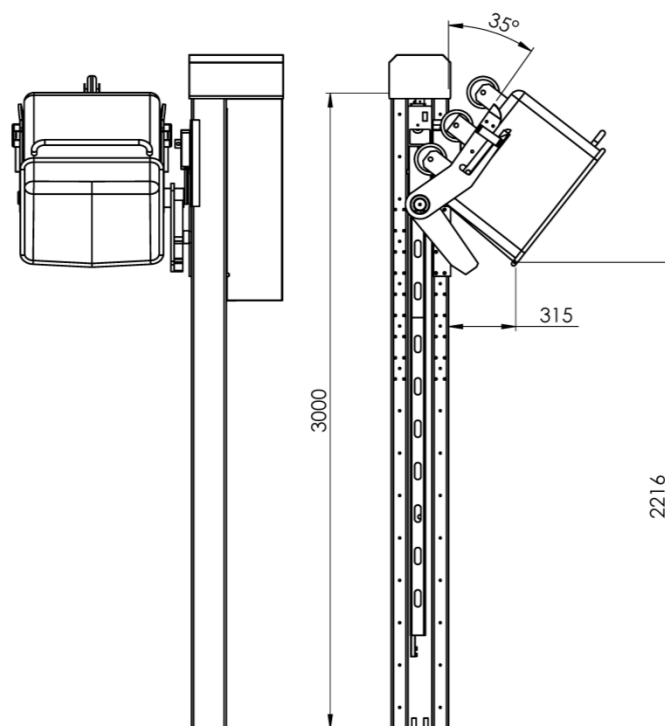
Hebe- und Kippvorrichtung Typ B mit Rollenkippsystem (Beispiel)
